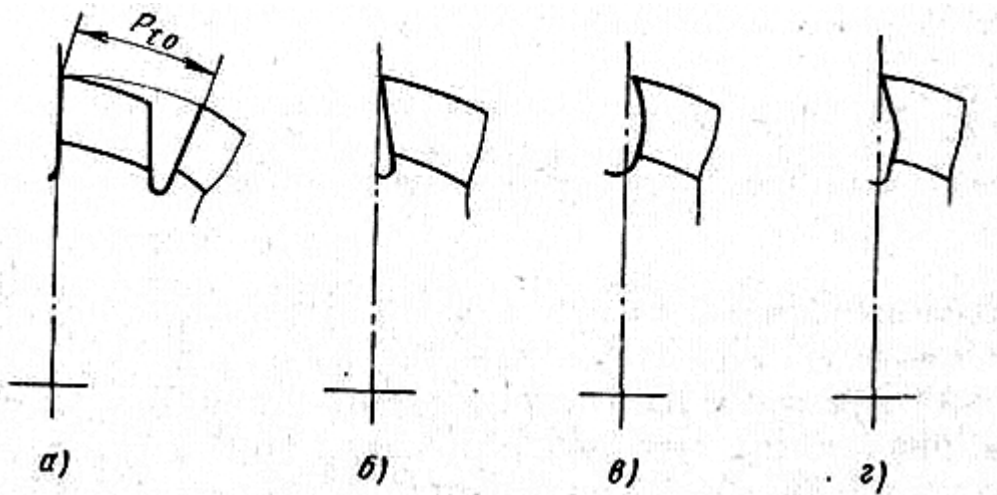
Форми зубів спеціальних шнекових фрез
